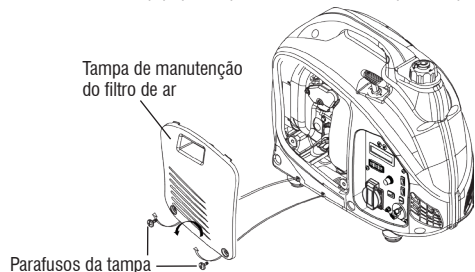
Removendo a tampa de manutenção do filtro de ar
